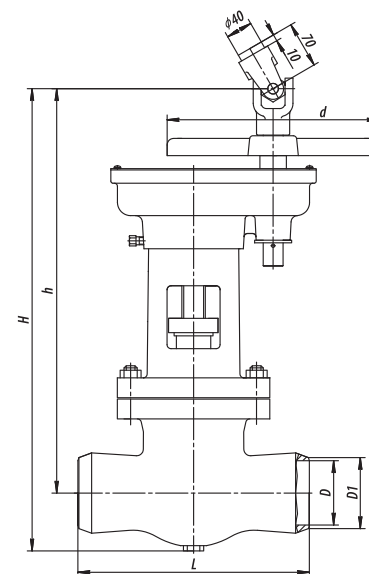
Задвижка DN80-100 с цилиндрическим редуктором
